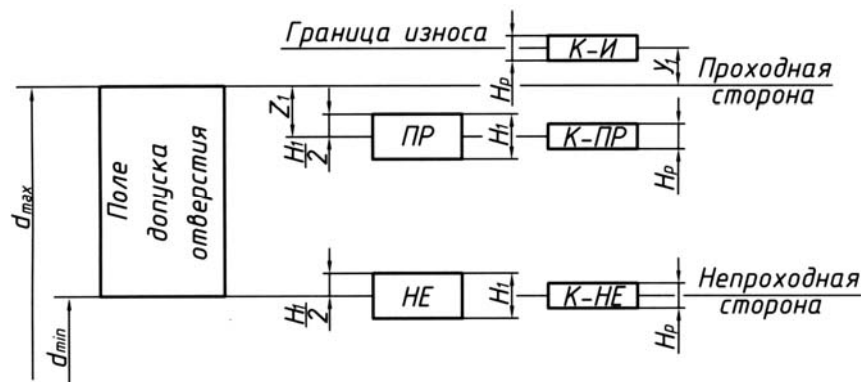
Схема полей допусков калибр-скобы для размеров до 180 мм
